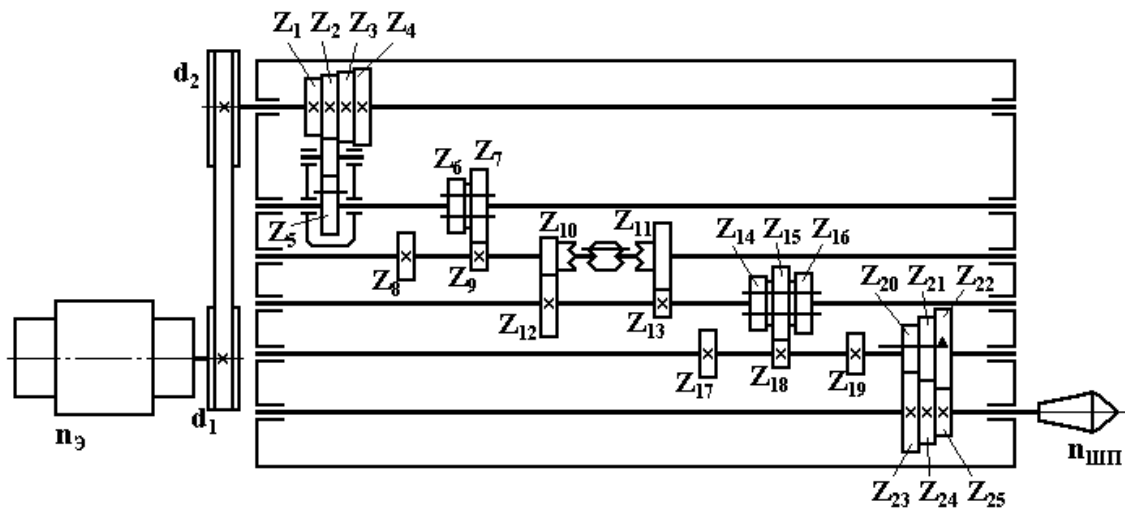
Кинематическая цепь главного движения условного станка (вариант № 49)
